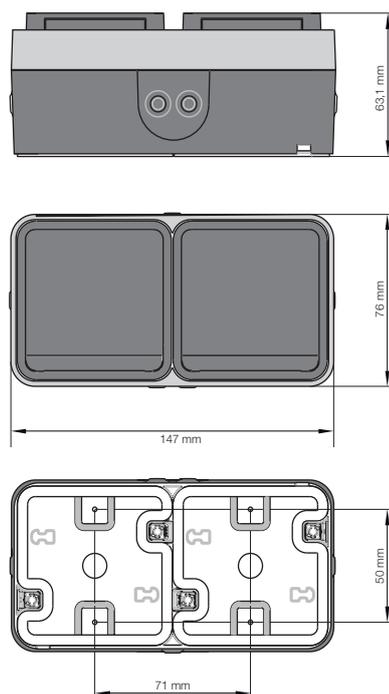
Steckdose SCHUKO 2fach mit Klappdeckel
